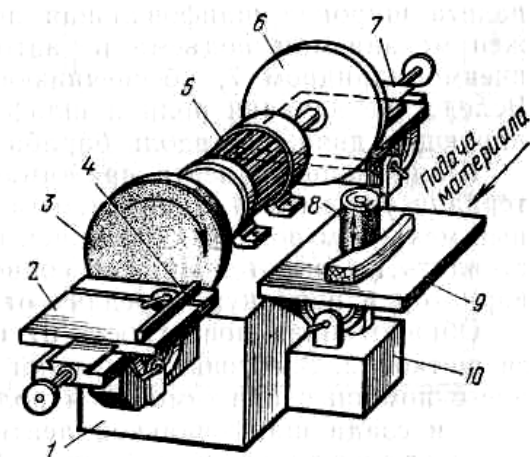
Комбинированный шлифовальный станок с двумя дисками и бобиной ШЛДБ-4:
